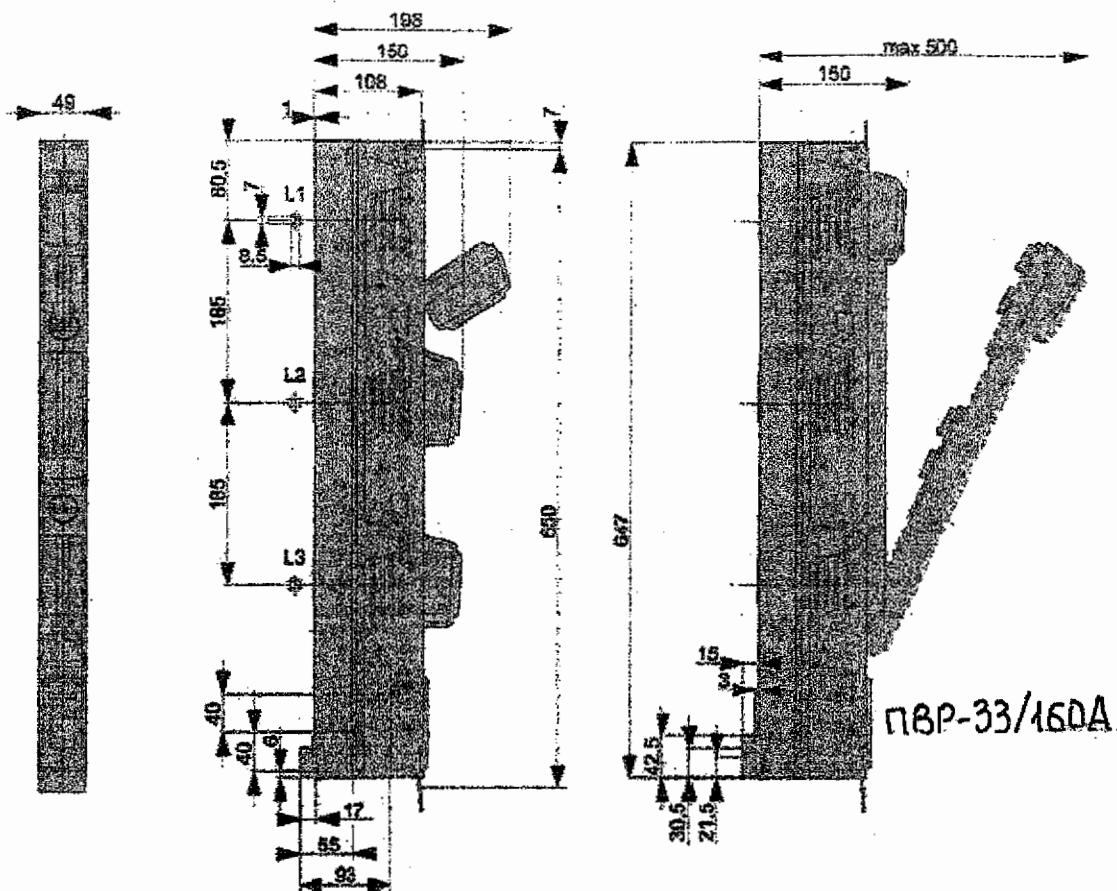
Габаритные, установочные и присоединительные размеры
